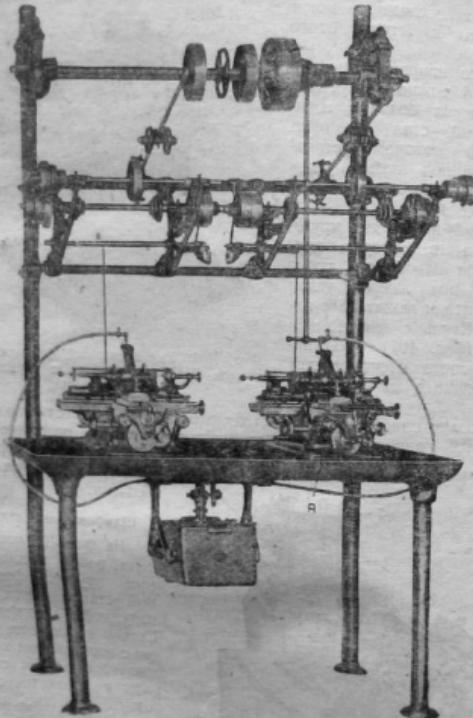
Универсальный фрезерный станок Шейблун. Работа с горизонтальным столом.
